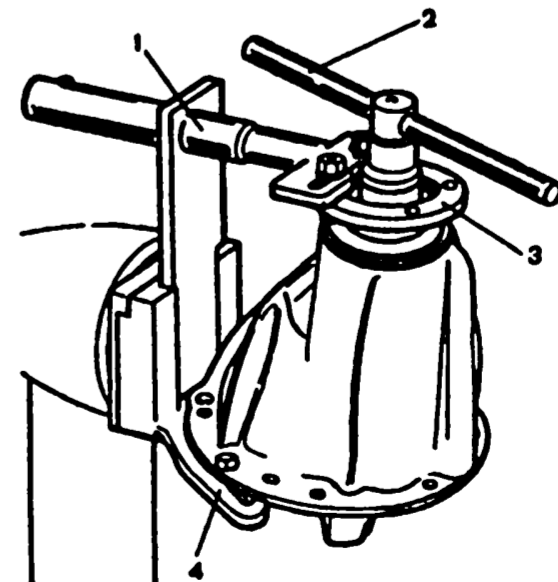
Отвертывание самоконтрящейся гайки ведущей шестерни: 1 - стопор для фиксирования фланца ведущей шестерни; 2 - торцевой ключ; 3 - фланец ведущей шестерни; 4 - кронштейн для крепления редуктора на стенде
